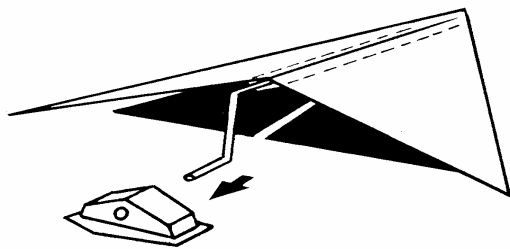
Montaggio delle aste ad "L" sugli aeratori.
